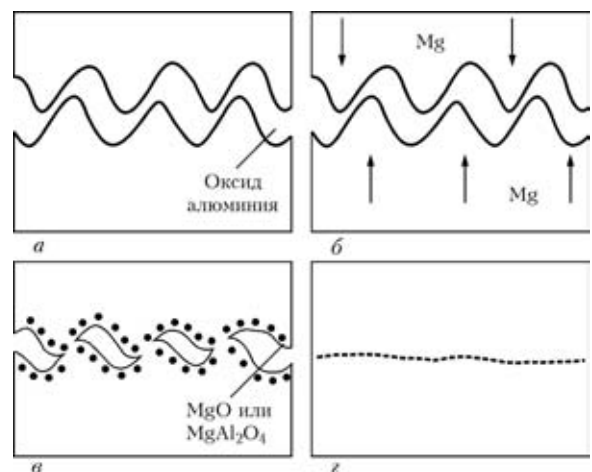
Схемы стадий образования сварного соединения [1]: а — физический контакт; б — диффузия магния к соединяемым поверхностям; в — взаимодействие магния с оксидом алюминия; г — металлическая связь
